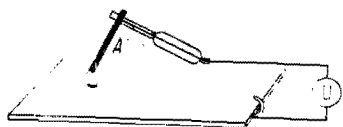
Сварка с сварочной проволокой в качестве электрода А.
